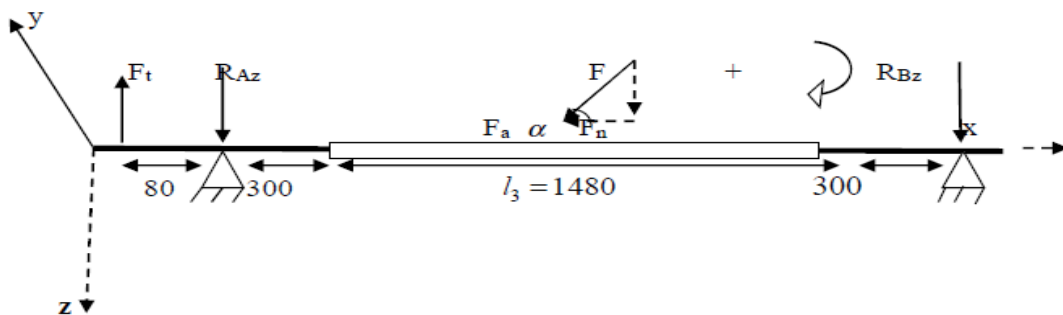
Schéma illustre les efforts sur la barre dans le plan (xoz).
